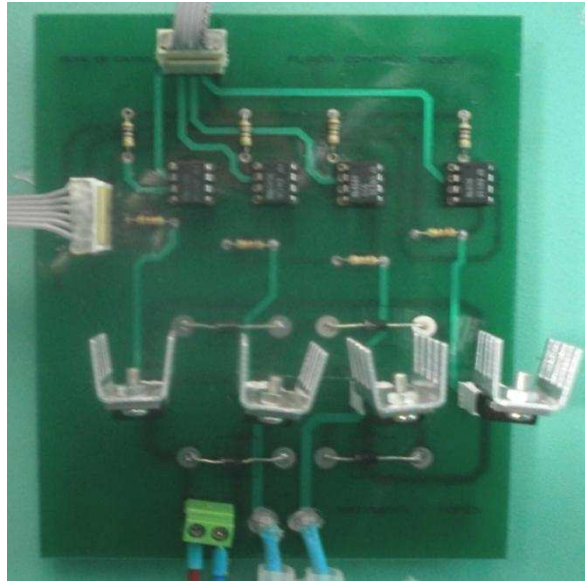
10 Tarjeta Ensamblada del circuito de control del Motor
